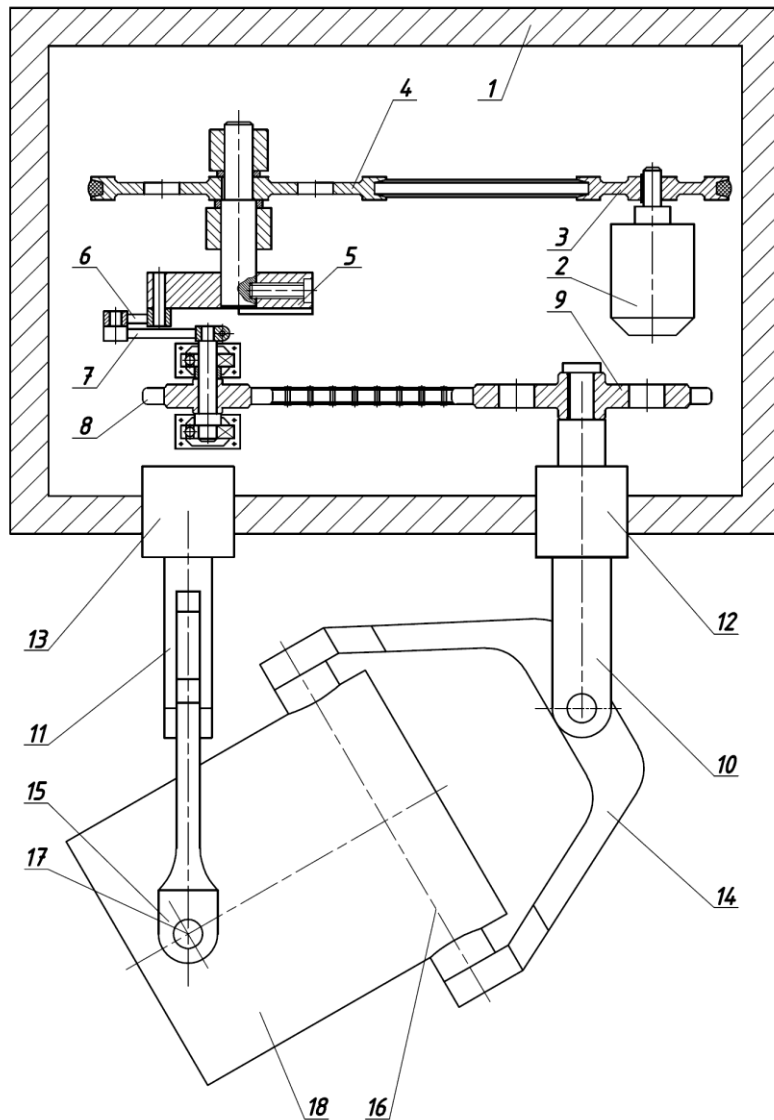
Машина для обробки деталей, в конструкції якої застосовується двохкривошипний привод
